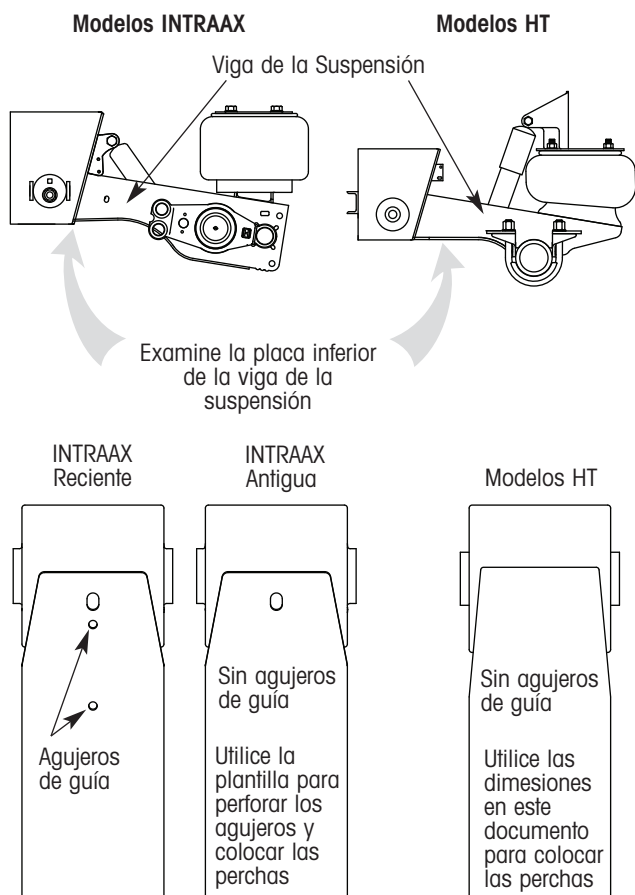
Apariencia de la placa inferior de la viga de la suspensión
